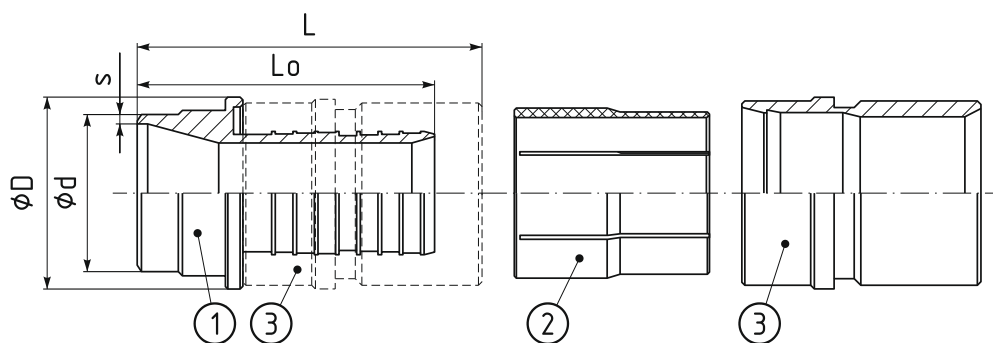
Пресс-фитинг с ПВ под сварку
